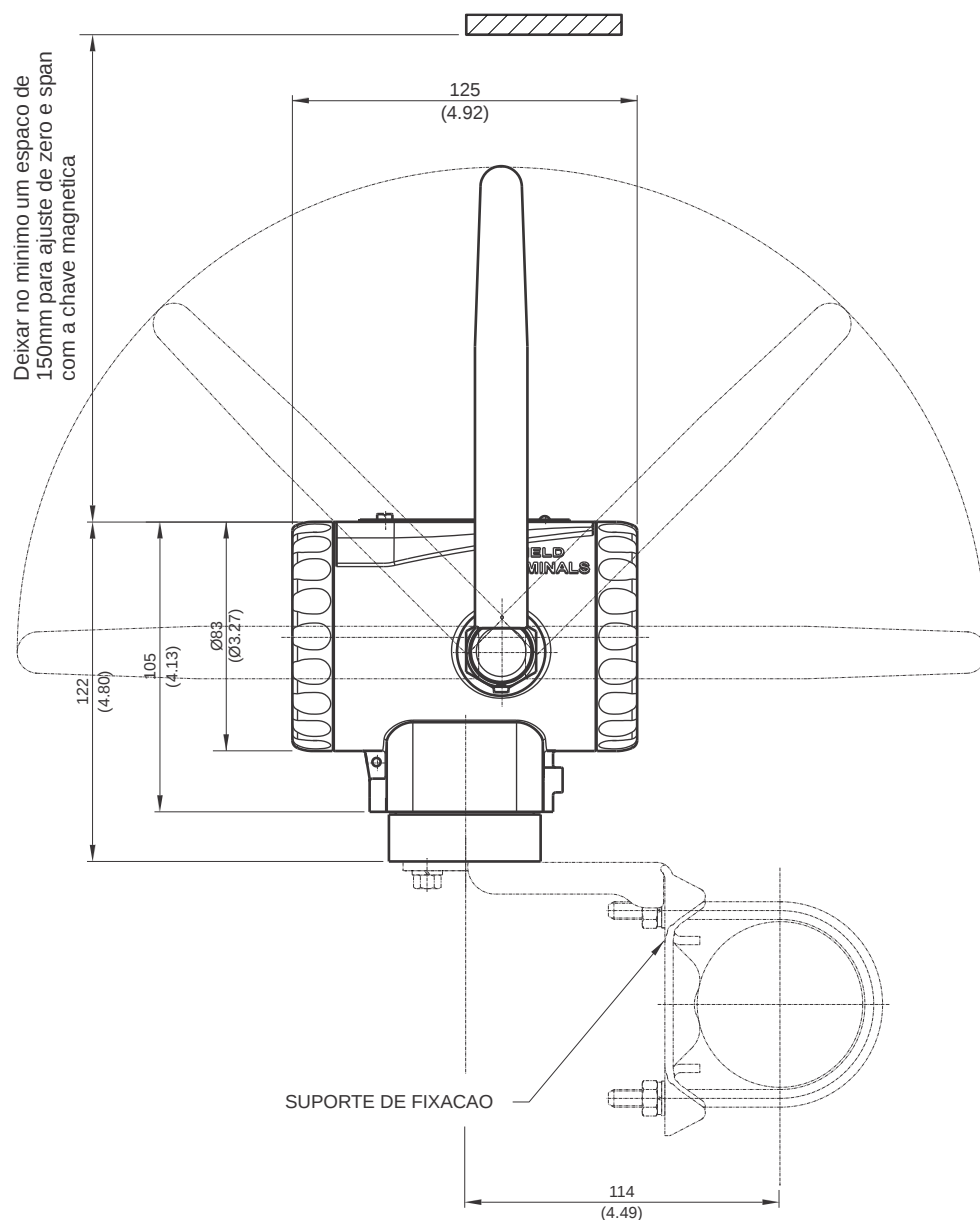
1 – Desenho Dimensional de Montagem do RP400 WirelessHART® na vertical
